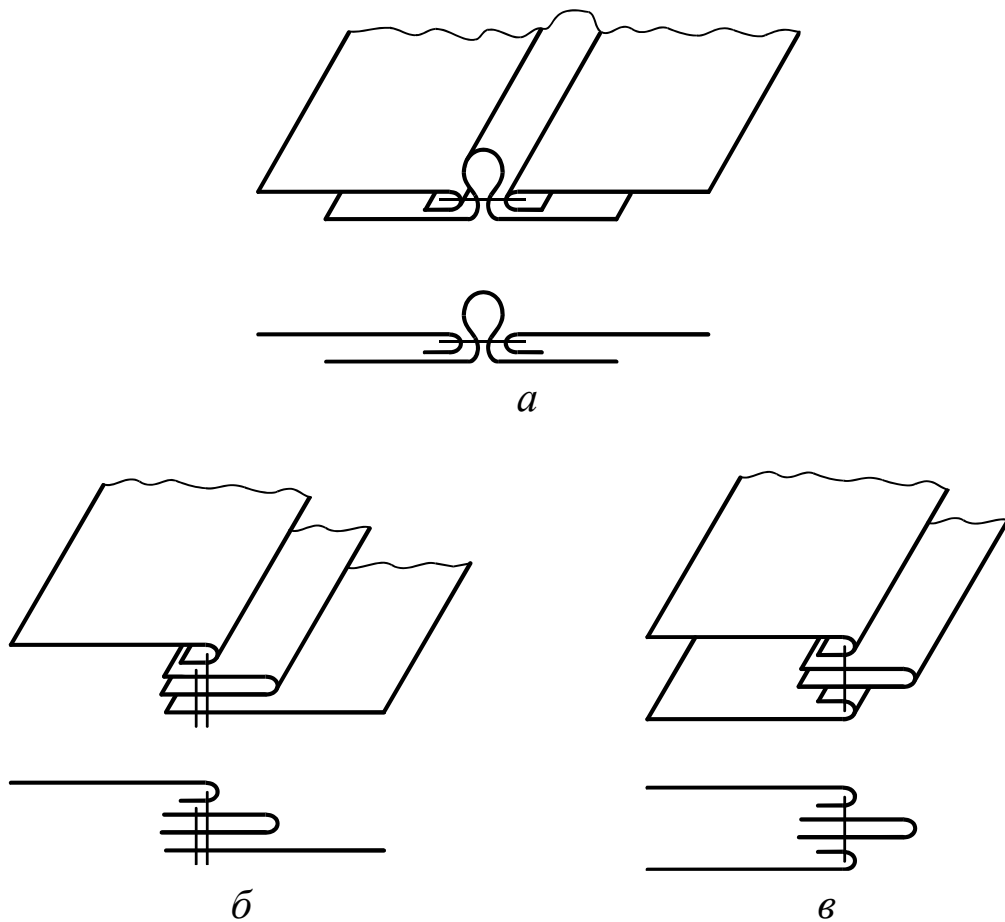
Шви оздоблюючі із кантом: а – зшивний; б – накладний; в – обшивний
